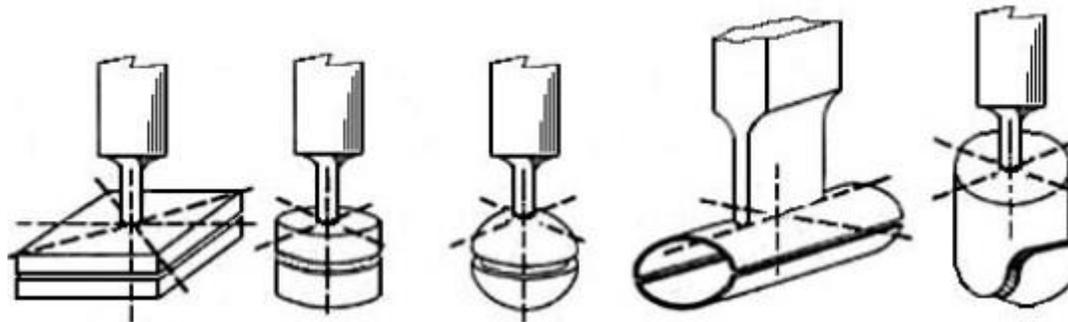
Расположение волновода при сварке деталей несложной формы
